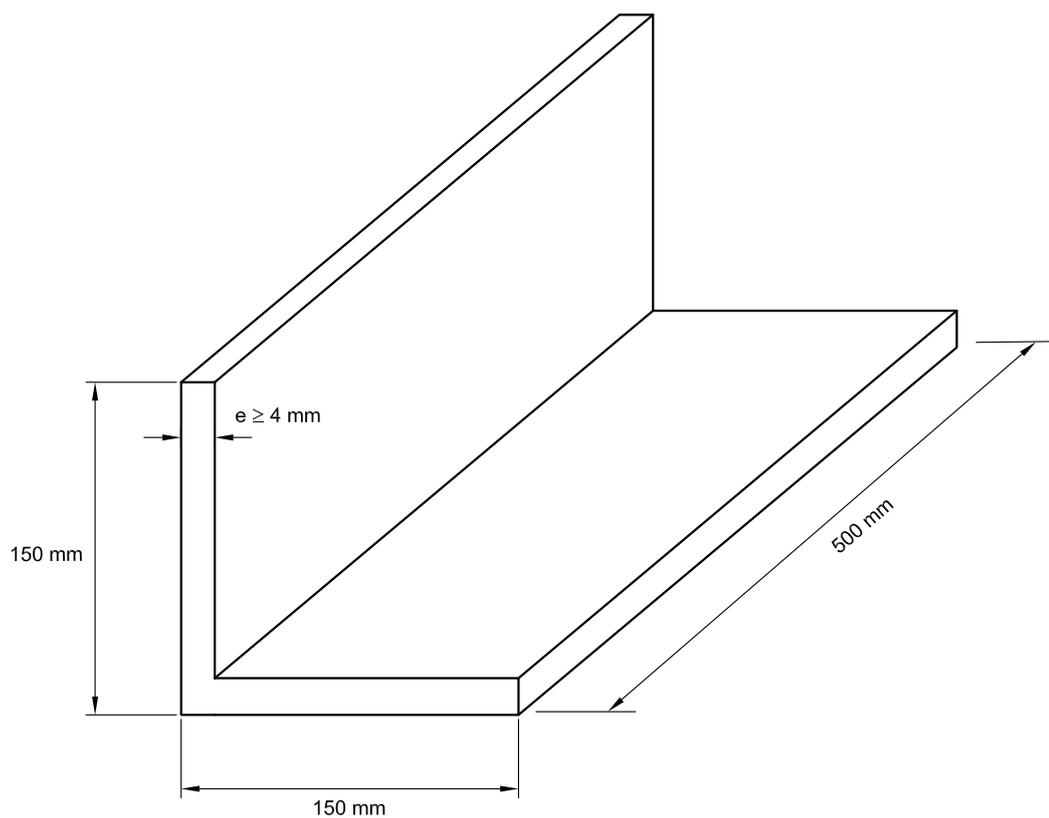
Perfil Cantoneira para Ensaio de Medição de Espessura
